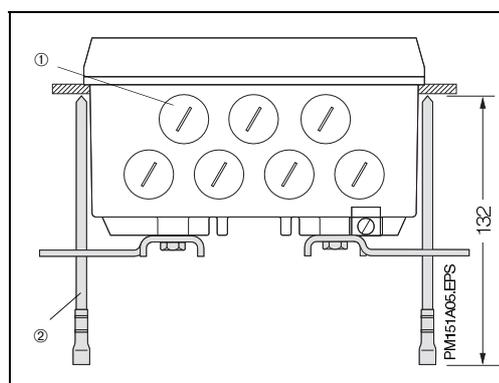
Partie inférieure du boîtier de terrain avec pattes de fixation en place pour le montage mural
